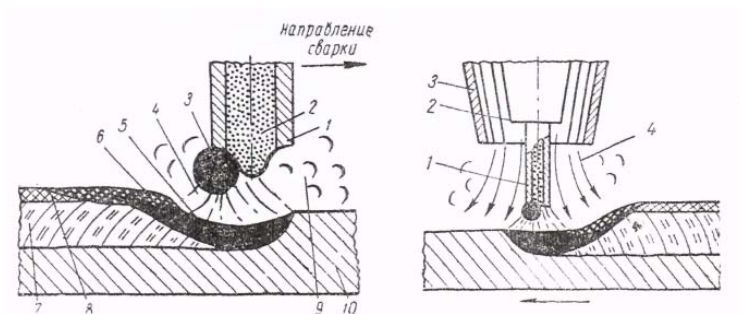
Схема процесса сварки самозащитной порошковой проволокой.
